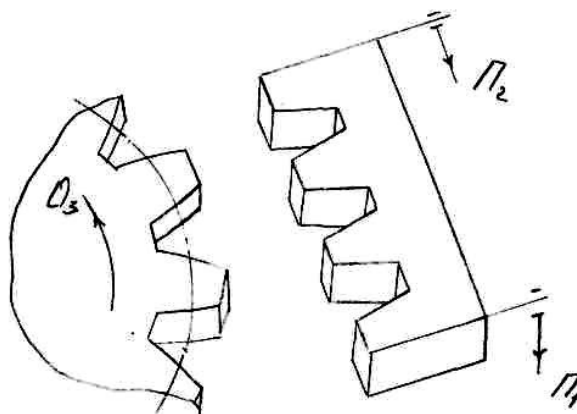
Схема обробки зуборізною гребінкою
